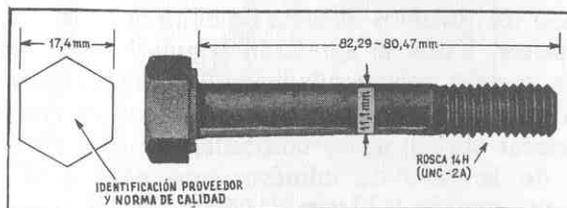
Tornillo de tapa de cilindros para motor 221 SP.
